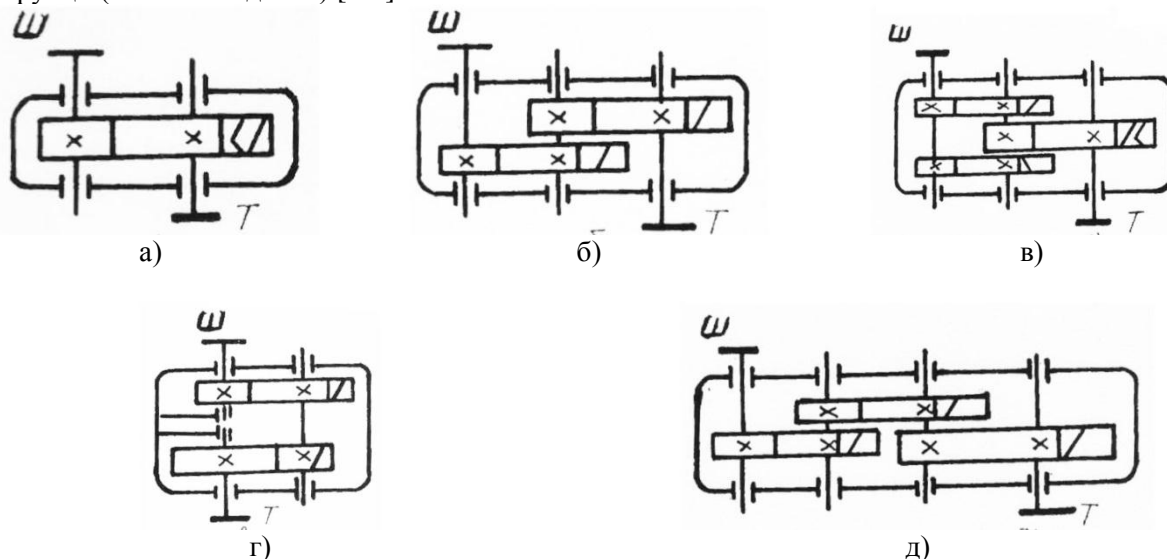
Кінематичні схеми циліндричних зубчастих редукторів (позначення на схемах: Ш – швидкохідний вал; Т – тихохідний вал)
